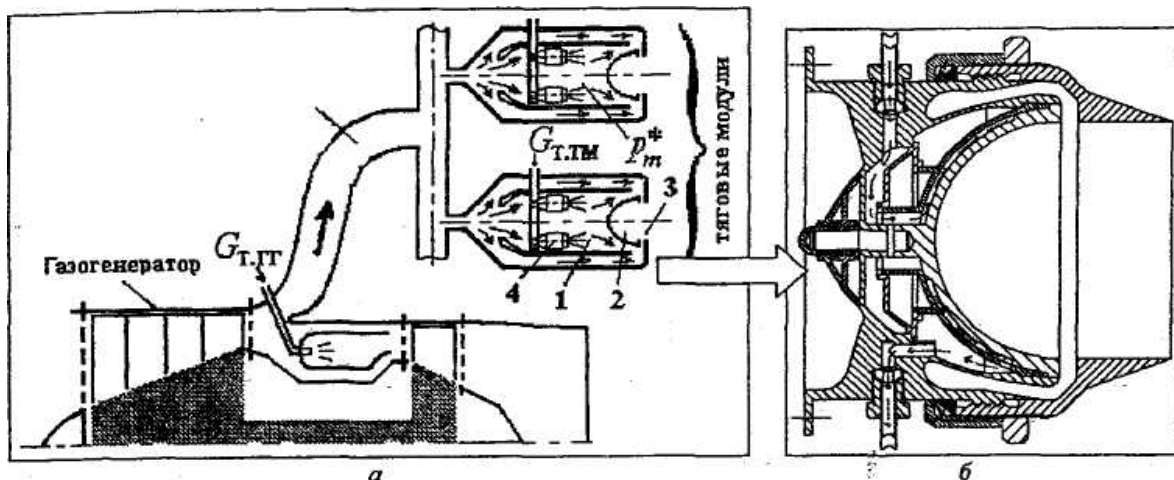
Схема устройства двигателя с двухстадийным сгоранием топлива: а – газогенератор с тяговыми модулями (1 – реактор; 2 – резонатор; 3 – кольцевое сопло; 4 – топливный смеситель); б – резонатор в сборе
